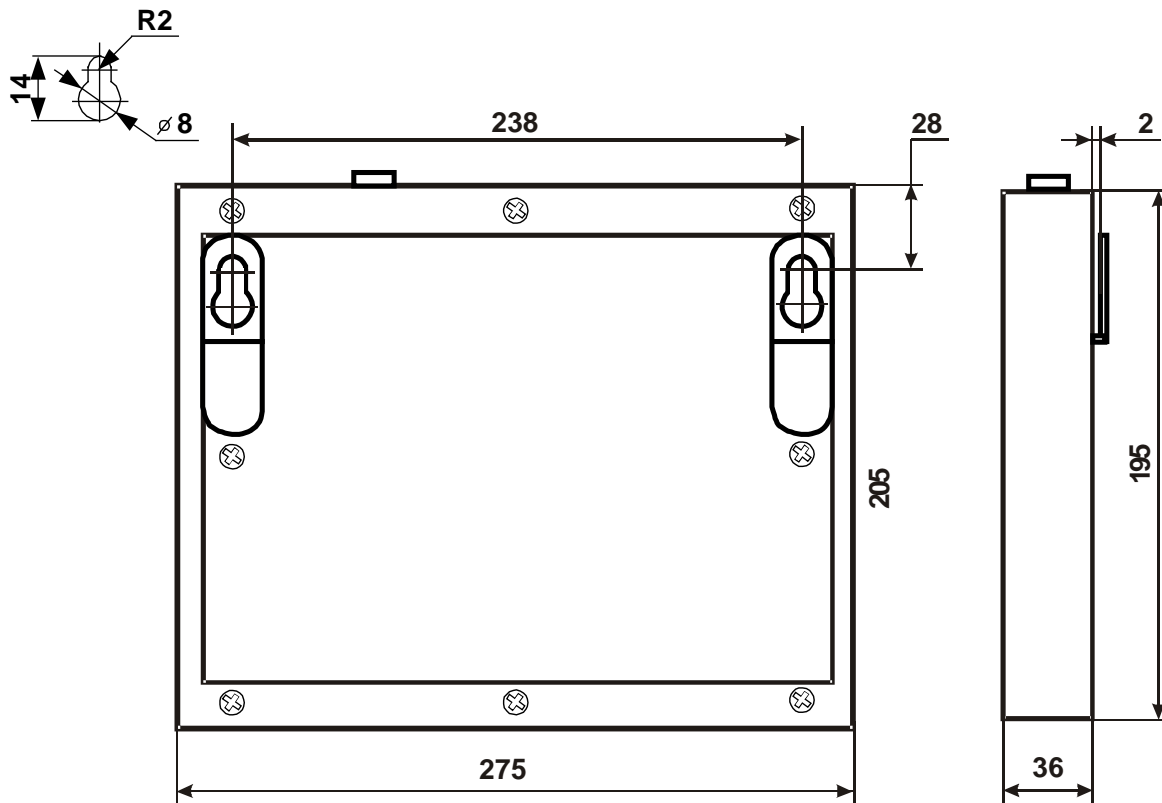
Габаритные и присоединительные размеры (вид со стороны крепления ППД)
